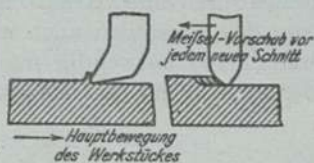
und 31. Arbeitsweise der Hobelmaschine.
